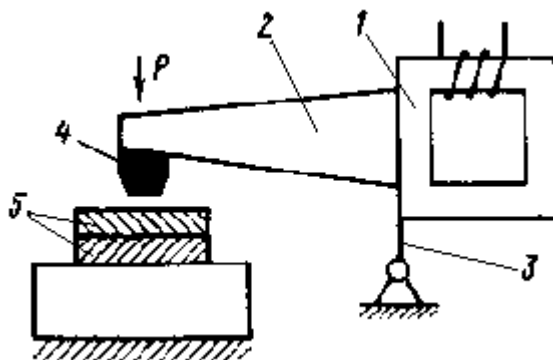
Схема ультразвуковой сварки:
